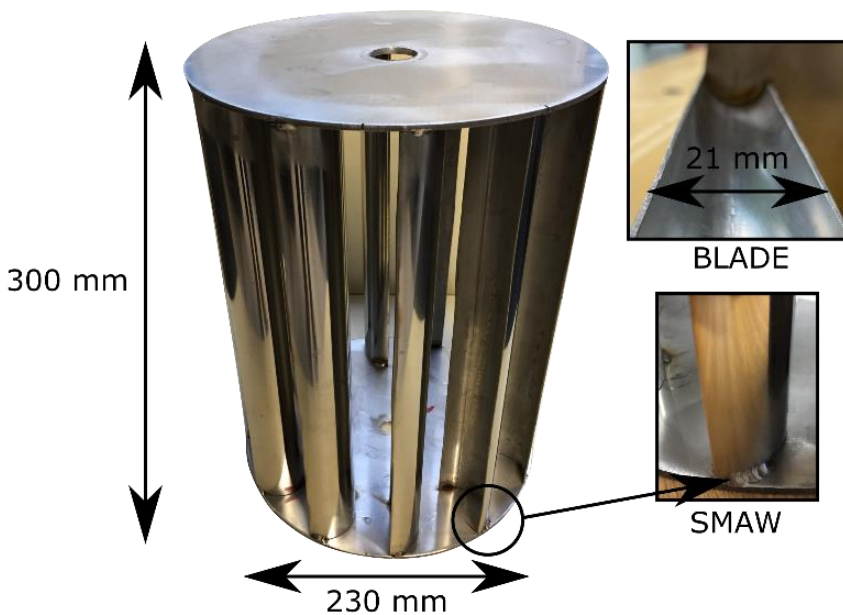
Dimensiones del rotor utilizado. [Fuente: Elaboración propia].
